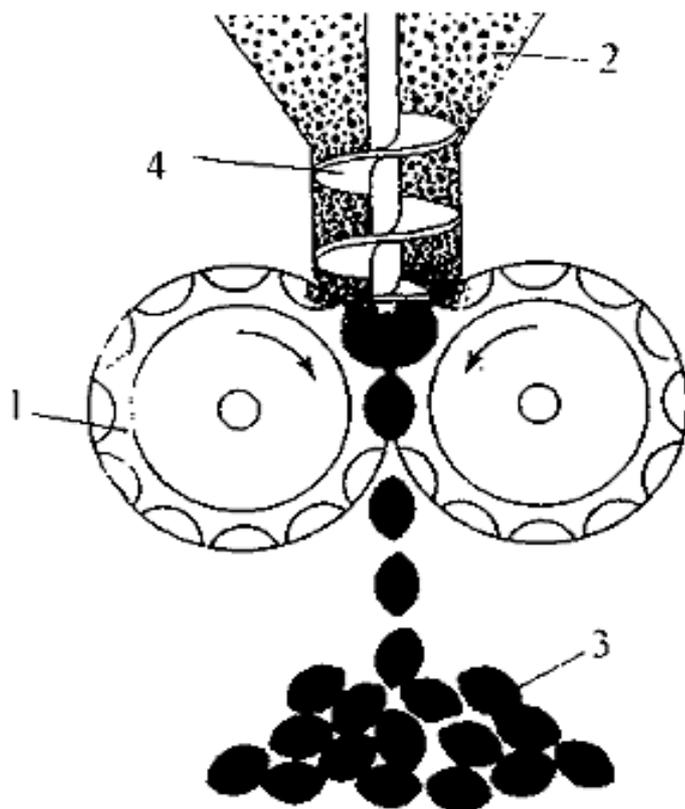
Внешний вид рабочих валков вальцевого прессы
